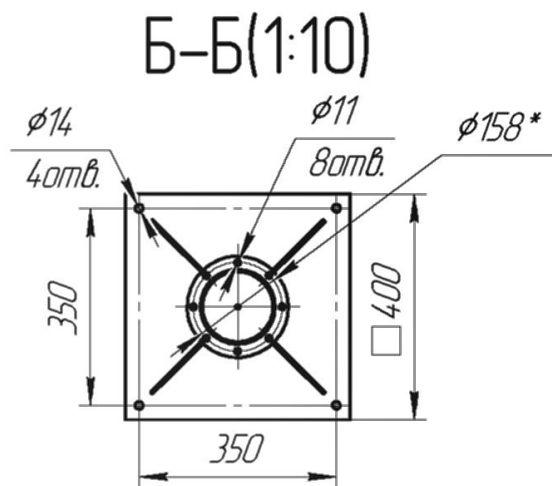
Габаритный чертеж ОПУ СУ. Сечение Б-Б
